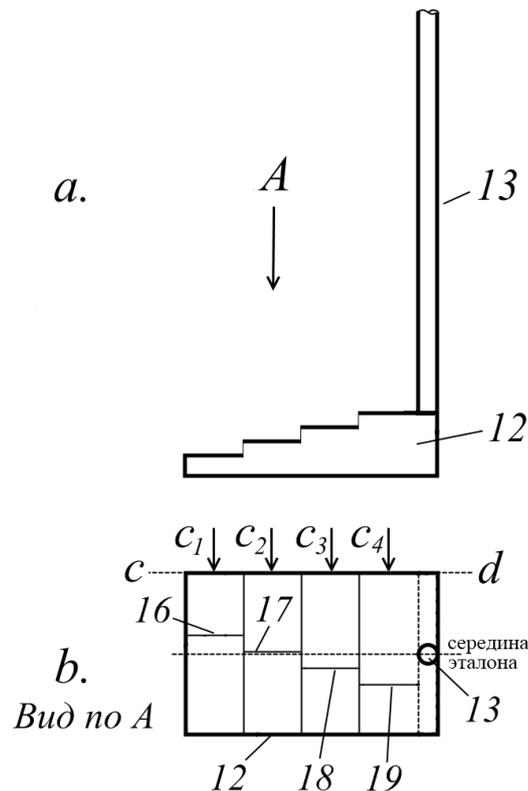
Схема калибровки измерений с помощью эталонной пластины.
